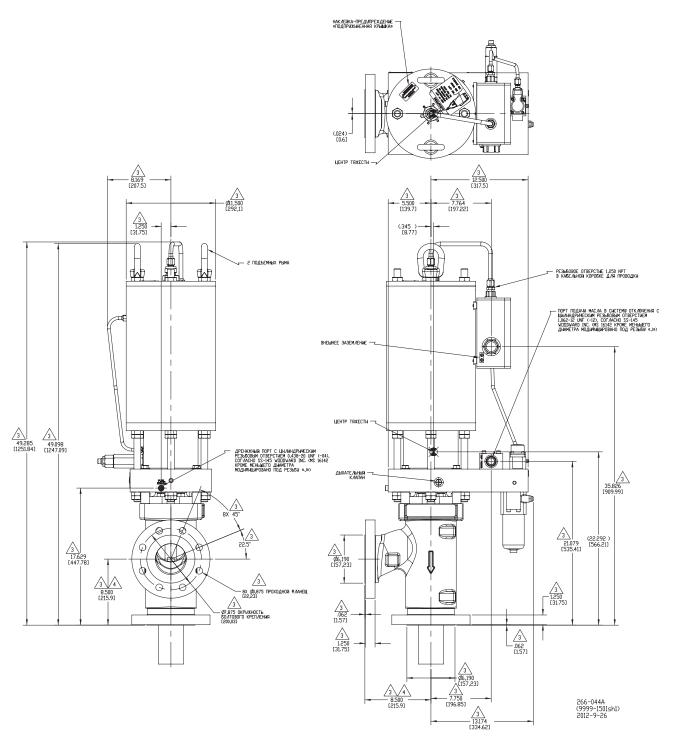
а. Габаритный чертеж регулятора SonicFlo (4 дюйма, класс 300)
